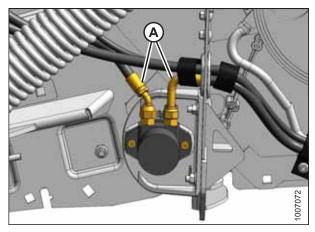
Moteur hydraulique arrière - Côté gauche
